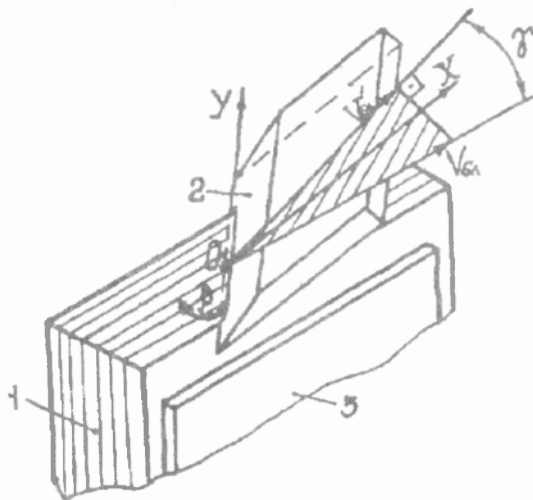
Схема обробки корінця книжкового блока віброножем:
